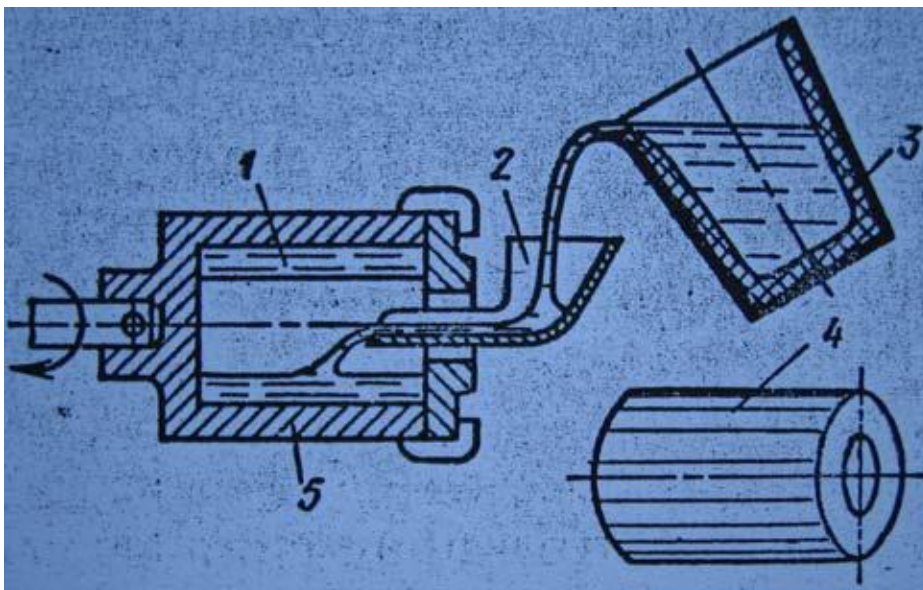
Схема отримання виливки при обертанні форми навколо горизонтальної осі. 1 - розплав, 2 - заливний жолоб, 3 - ківш, 4-виливок, 5 - форма.
